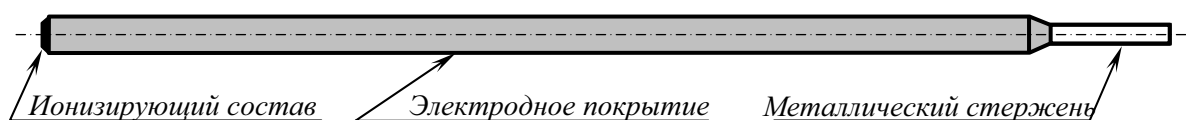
Внешний вид покрытого электрода для ручной дуговой сварки
